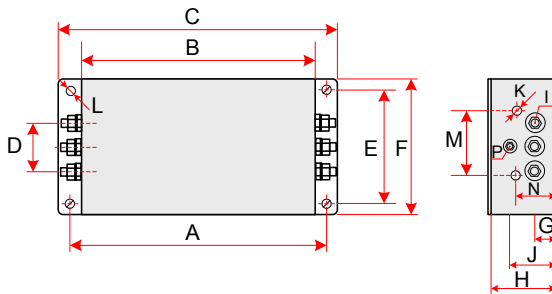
竖力滤波器 50-180A 尺寸图 (单位: mm)
